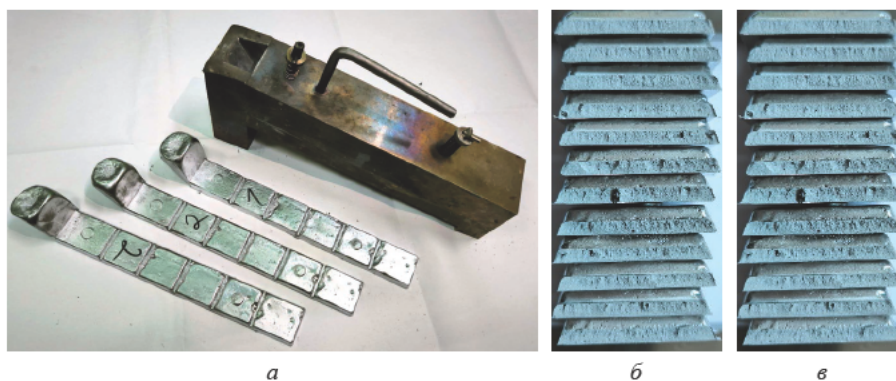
Кокиль для K-mold-теста и получаемые образцы (а); образцы изломов до металлургической обработки сплава (б); образцы изломов после металлургической обработки сплава и фильтрации через ПКФ (в)
